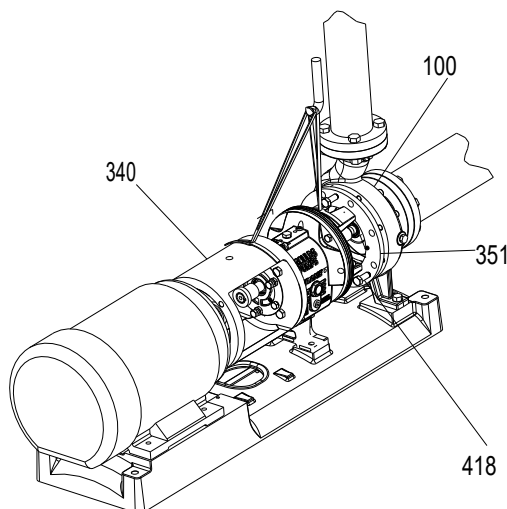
Desserrer les vis de bridage et les vis de déblocage sur le boîtier de roulement
